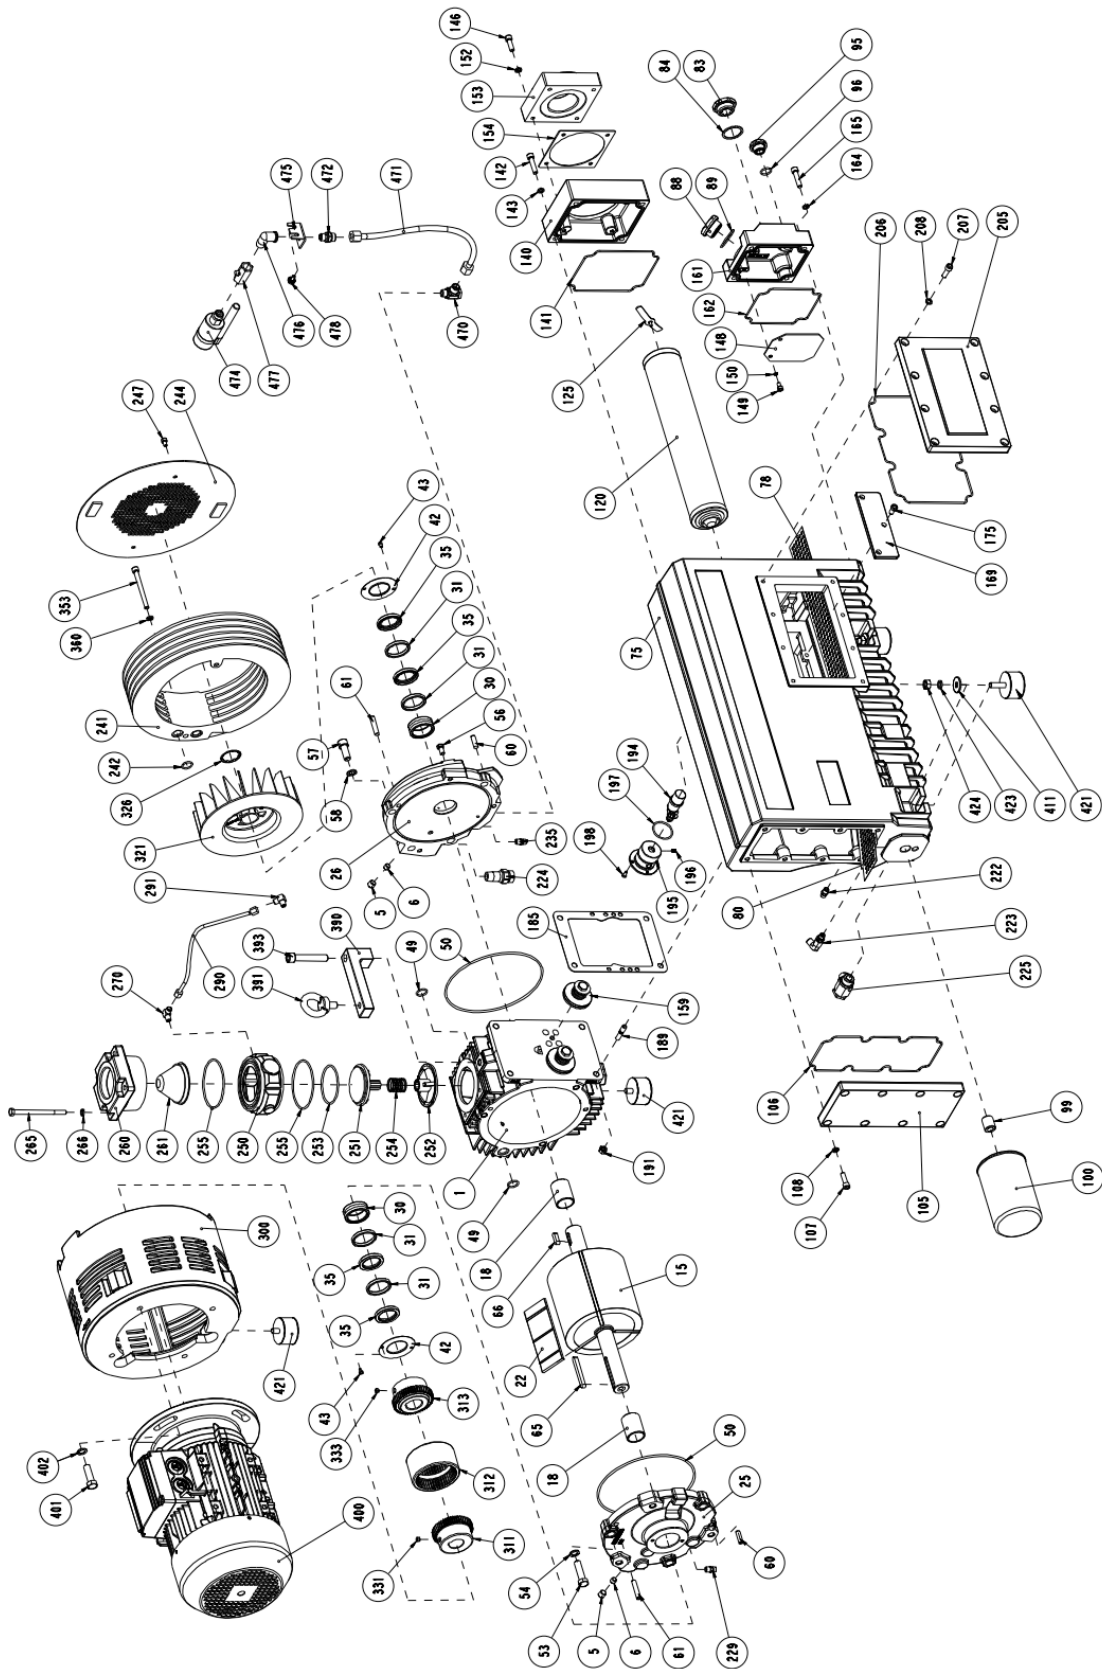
Explosionszeichnung der Modelle -0160 / -0200
